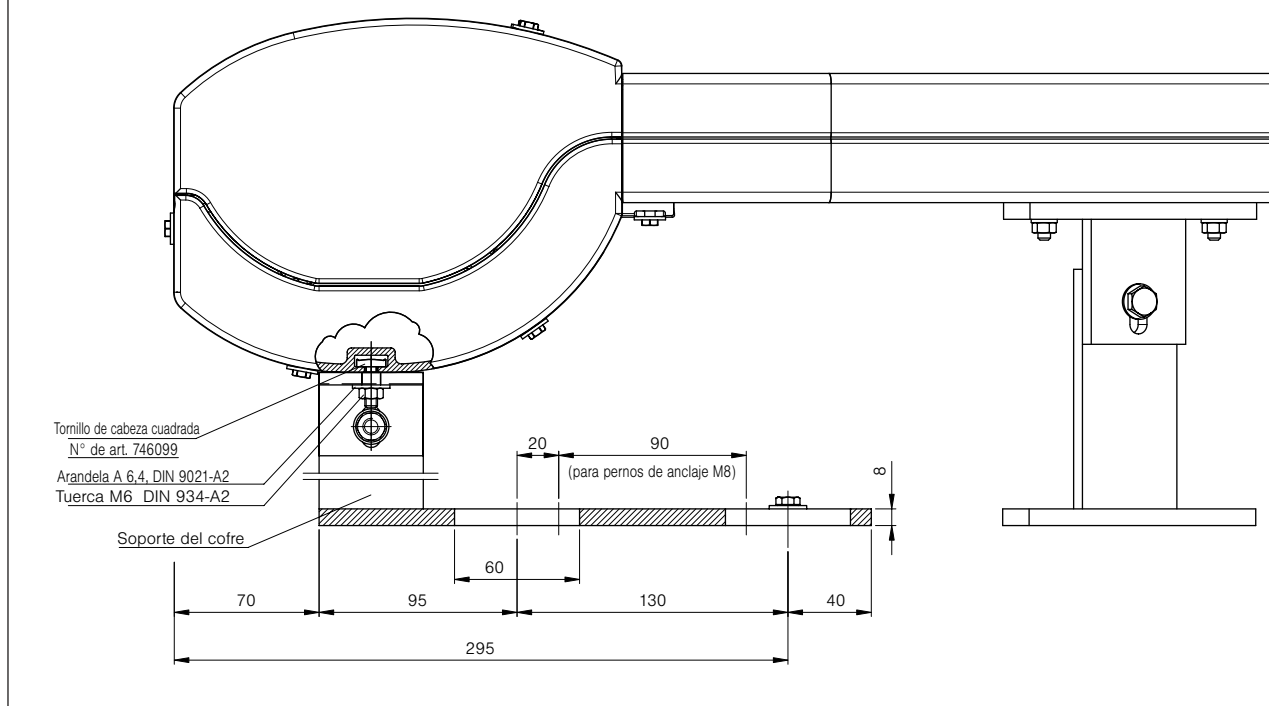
Montaje estribo estabilizador y apoyo de la cubierta protectora
